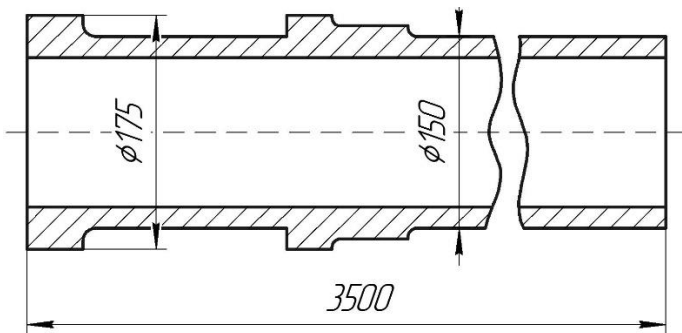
Конструкция из цилиндра, изготавливаемого из поковки
